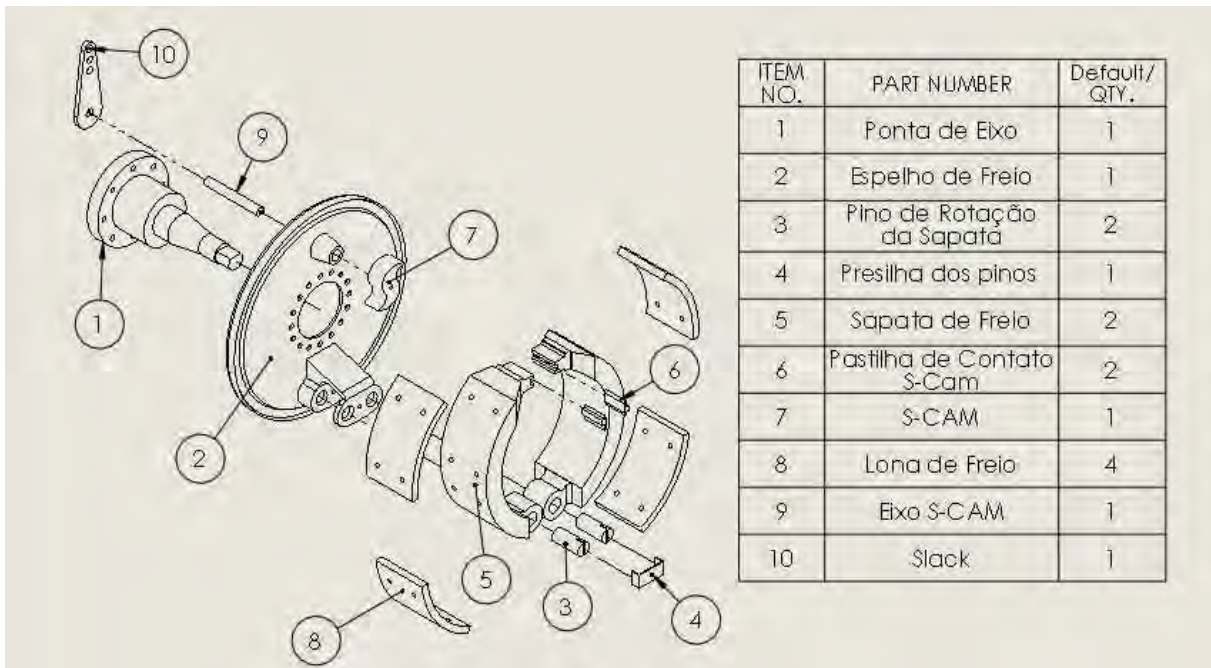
Vista explodida da montagem do freio S-Cam do desenho em SolidWorks® juntamente com a lista dos seus componentes.
